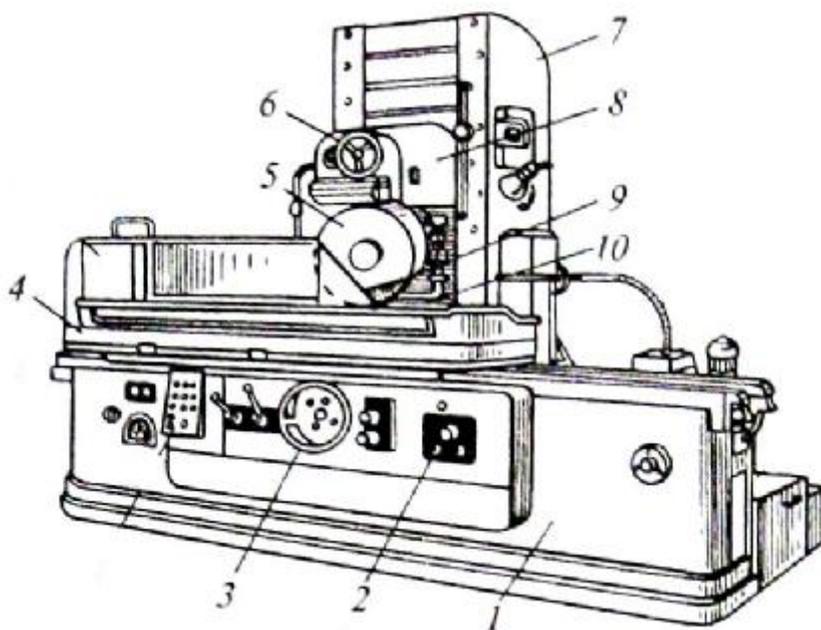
Станок плоскошлифовальный: 1 – станина; 2 – пульт управления; 3 – маховик ручного перемещения стола; 4 – стол; 5 – кожух шлифовального круга; 6 – маховик перемещения (вертикального) шлифовальной бабки 8; 7 – стойка; 9 – круг шлифовальный; 10 – плита магнитная
